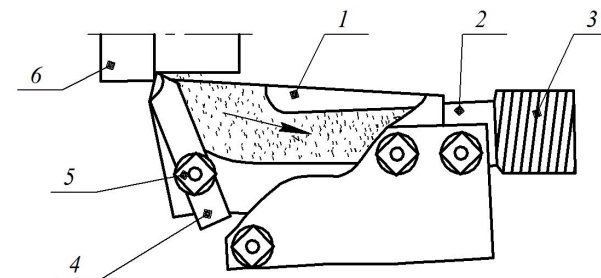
Резец-пылестружкоприемник к токарному станку:
